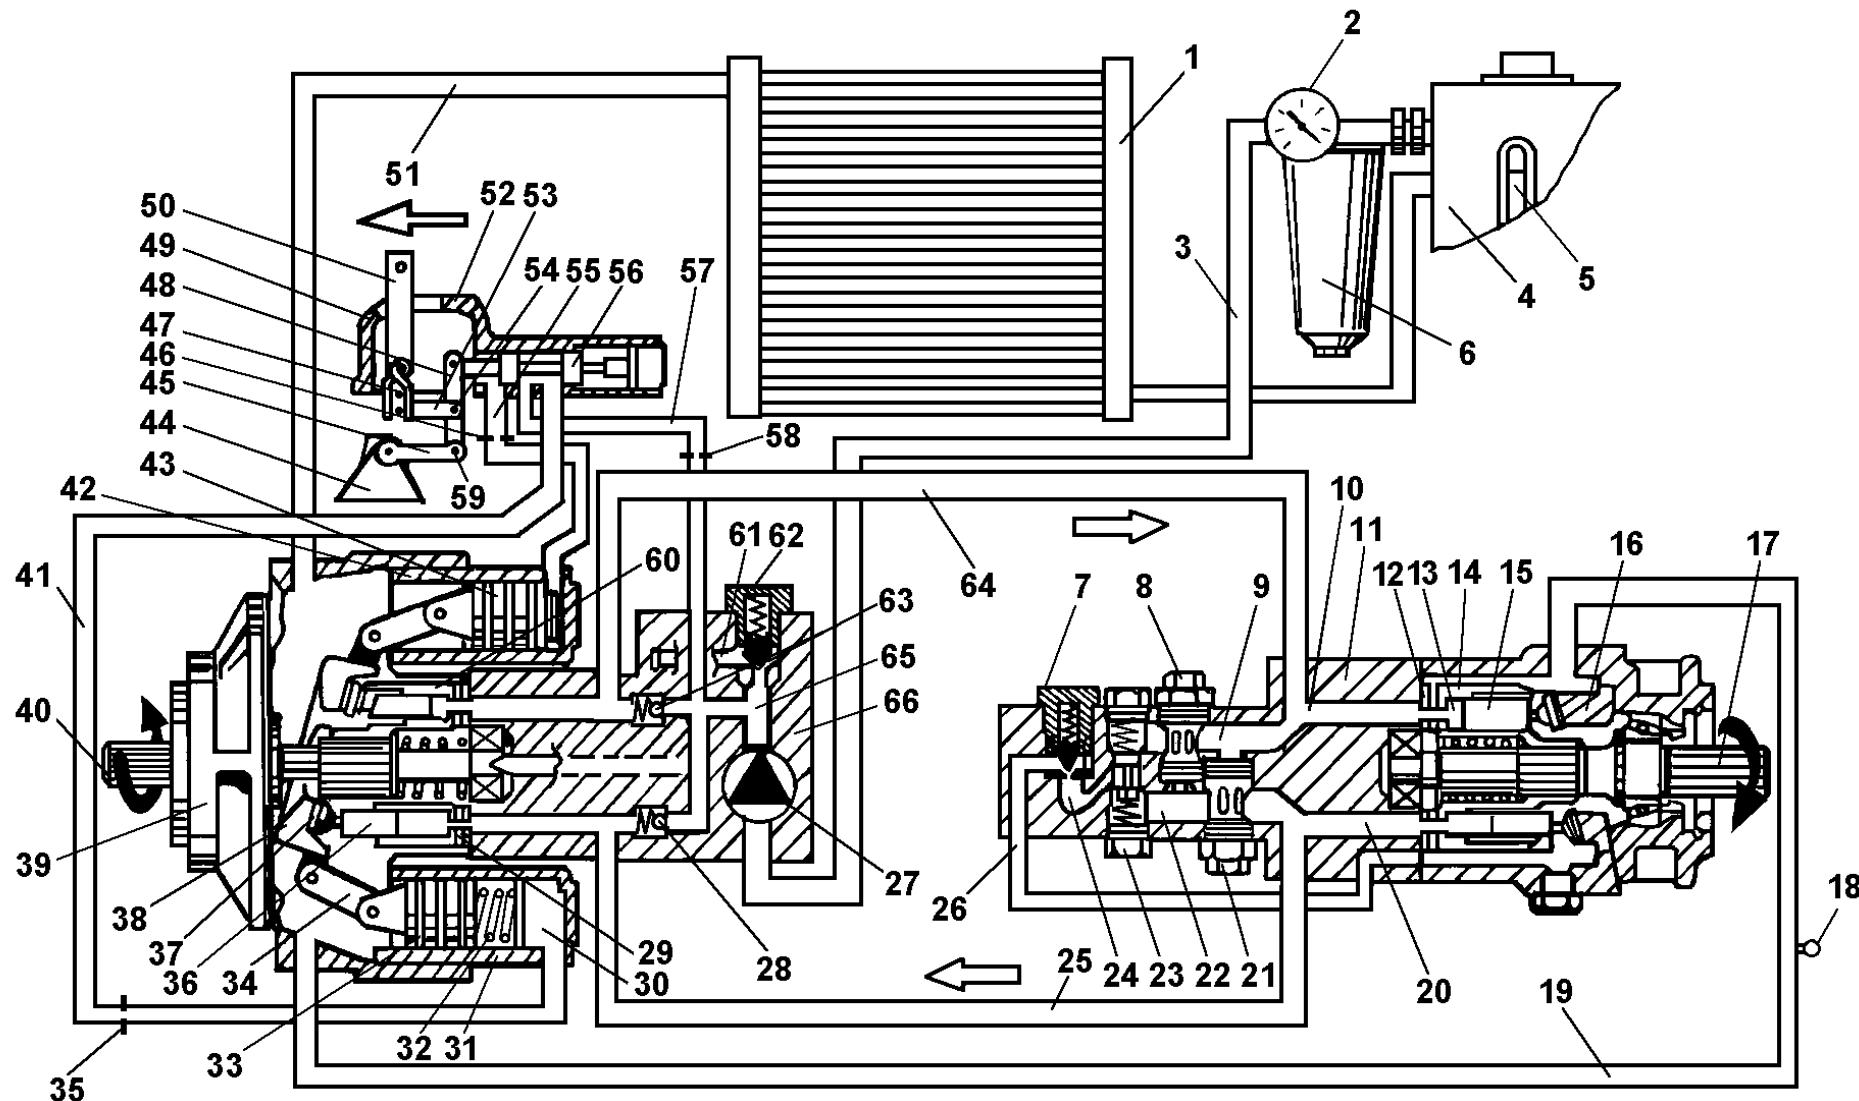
Конструктивная схема привода ГСТ-90 (движение вперед):
